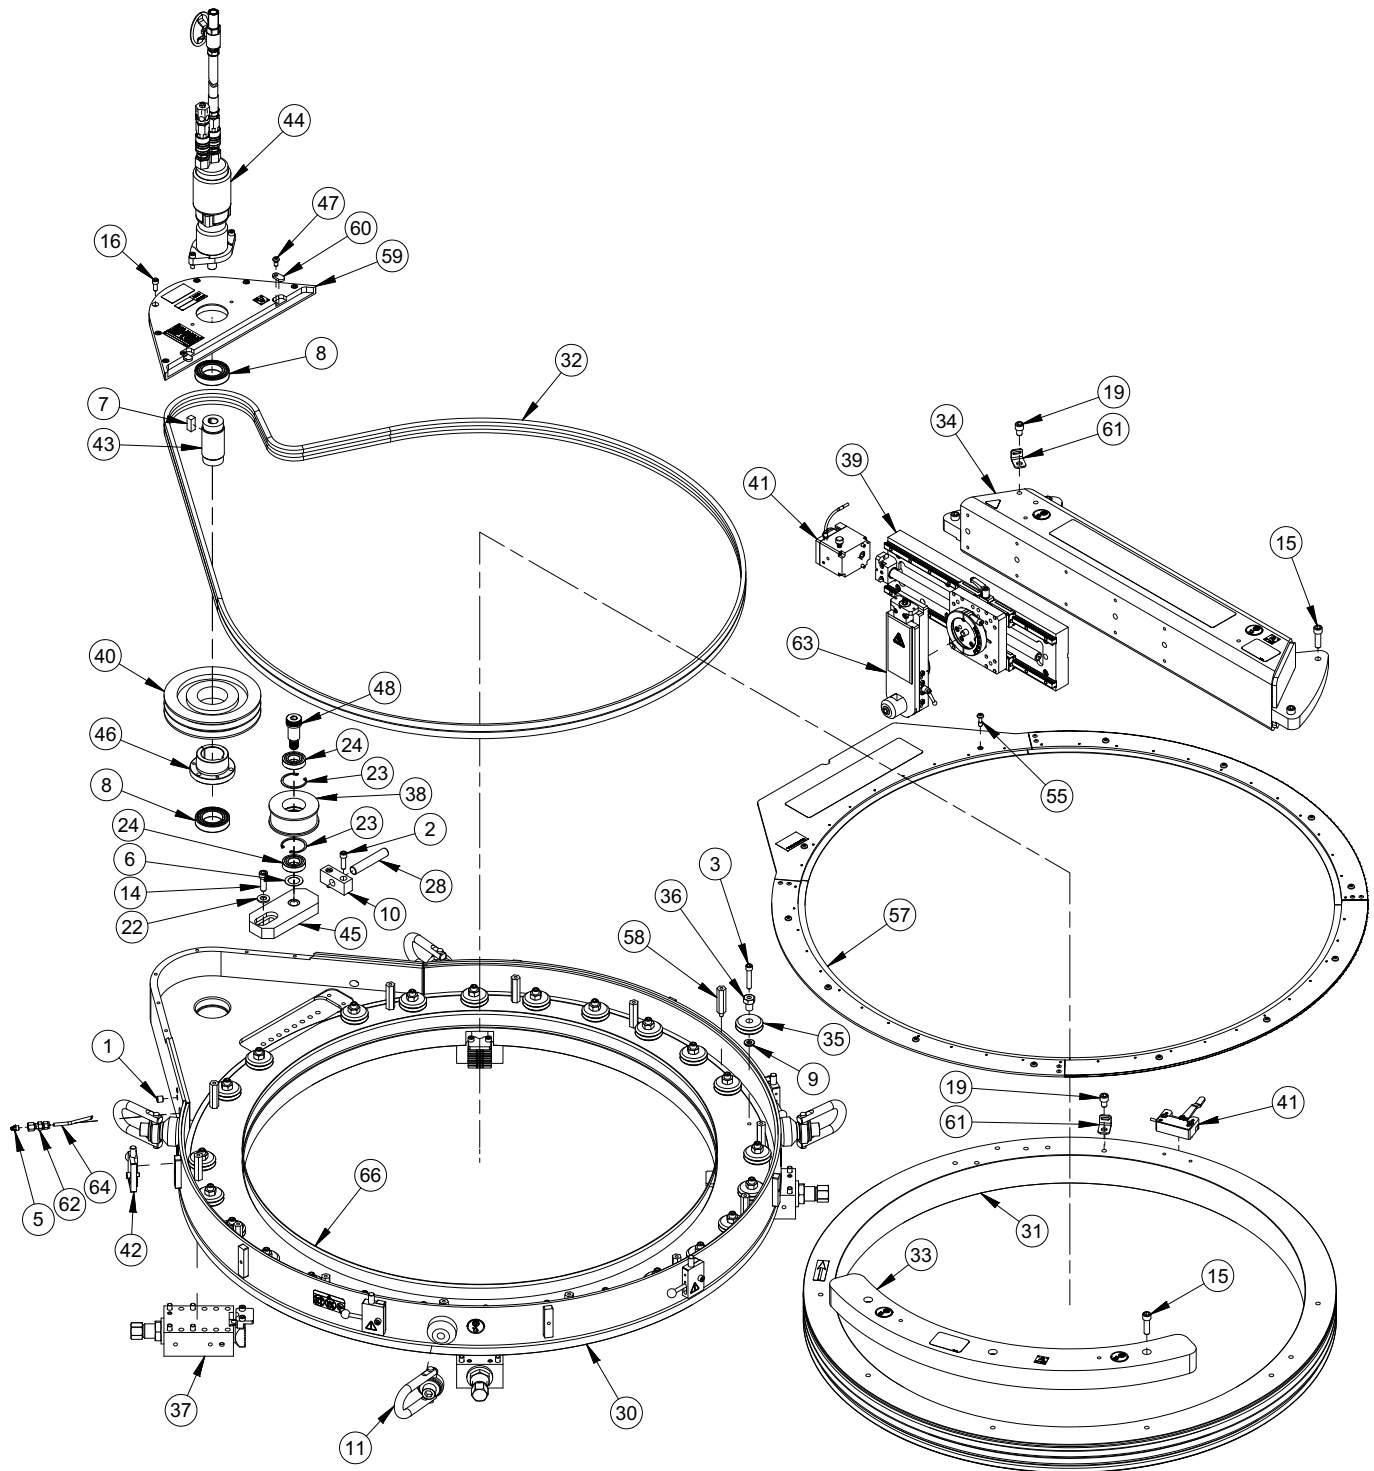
CONJUNTO DE LA ODF40 SPEED FACER (N/P 86870)
